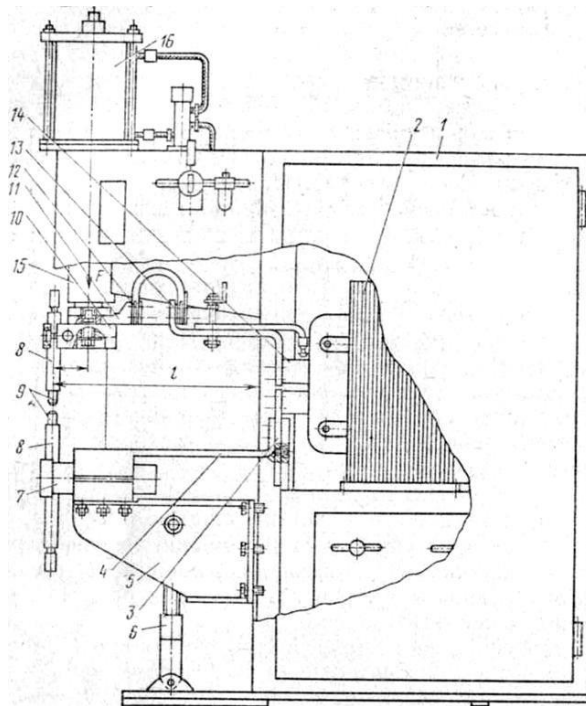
Машина точечной сварки МТ – 604
